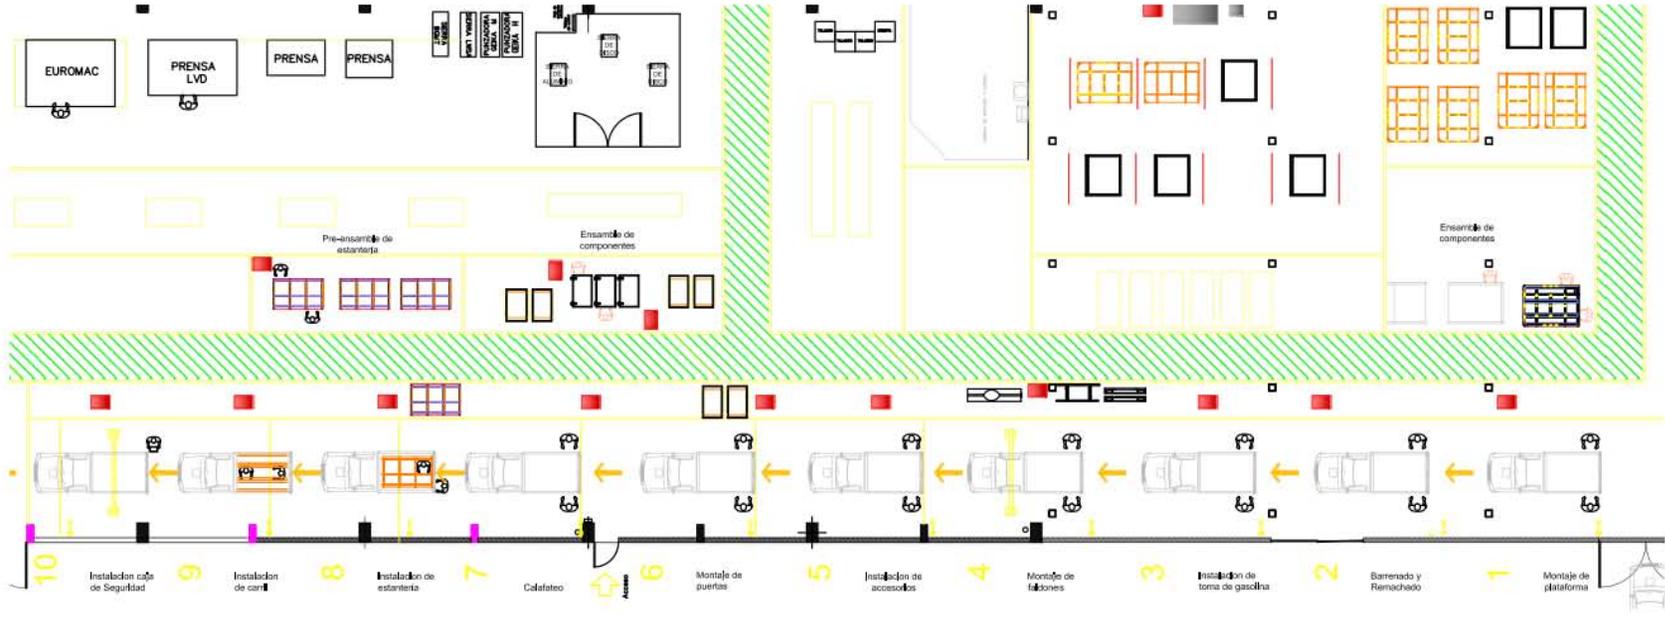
LAYOUT de la línea de ensamble. Realizado por la empresa.
